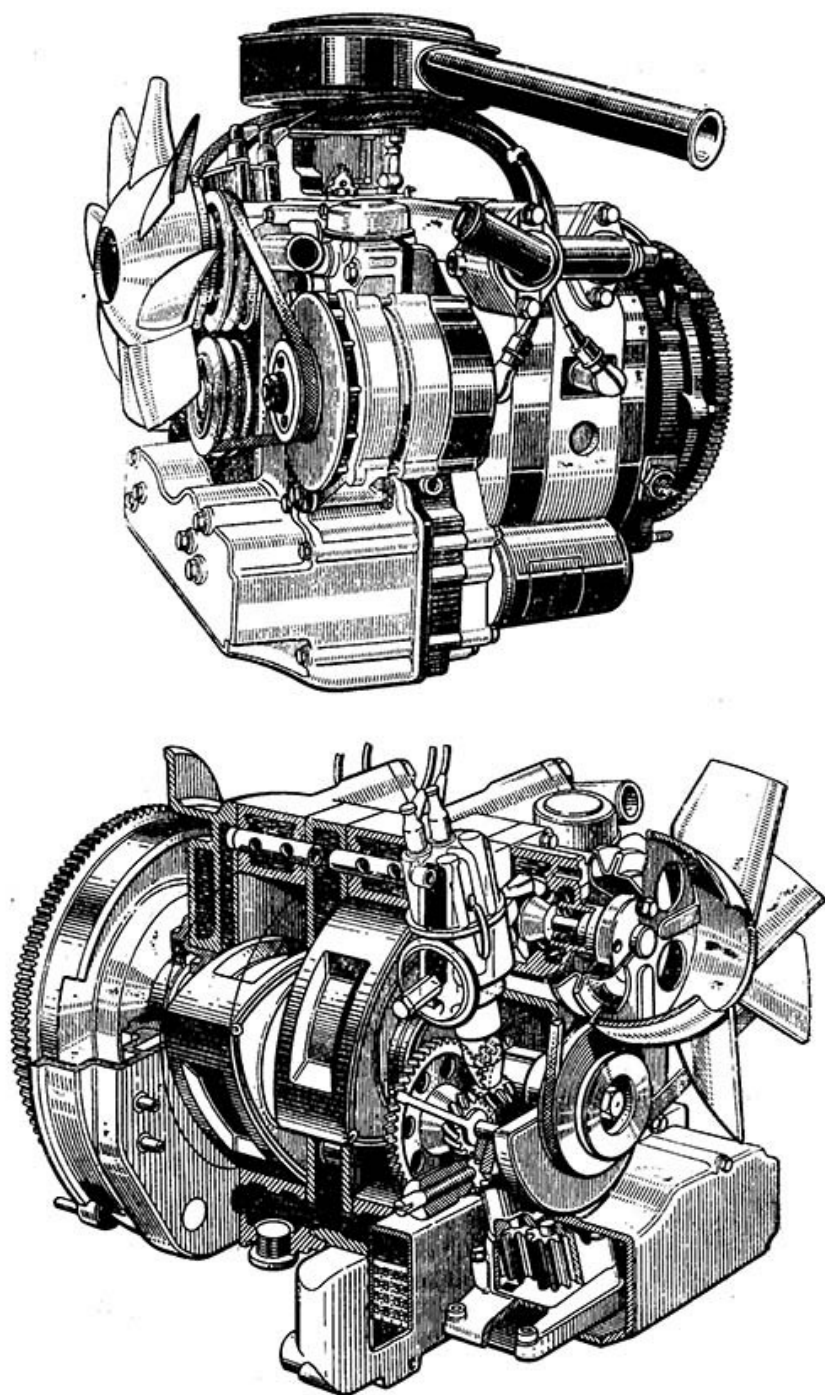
Общий вид двухроторного двигателя ККМ-512
